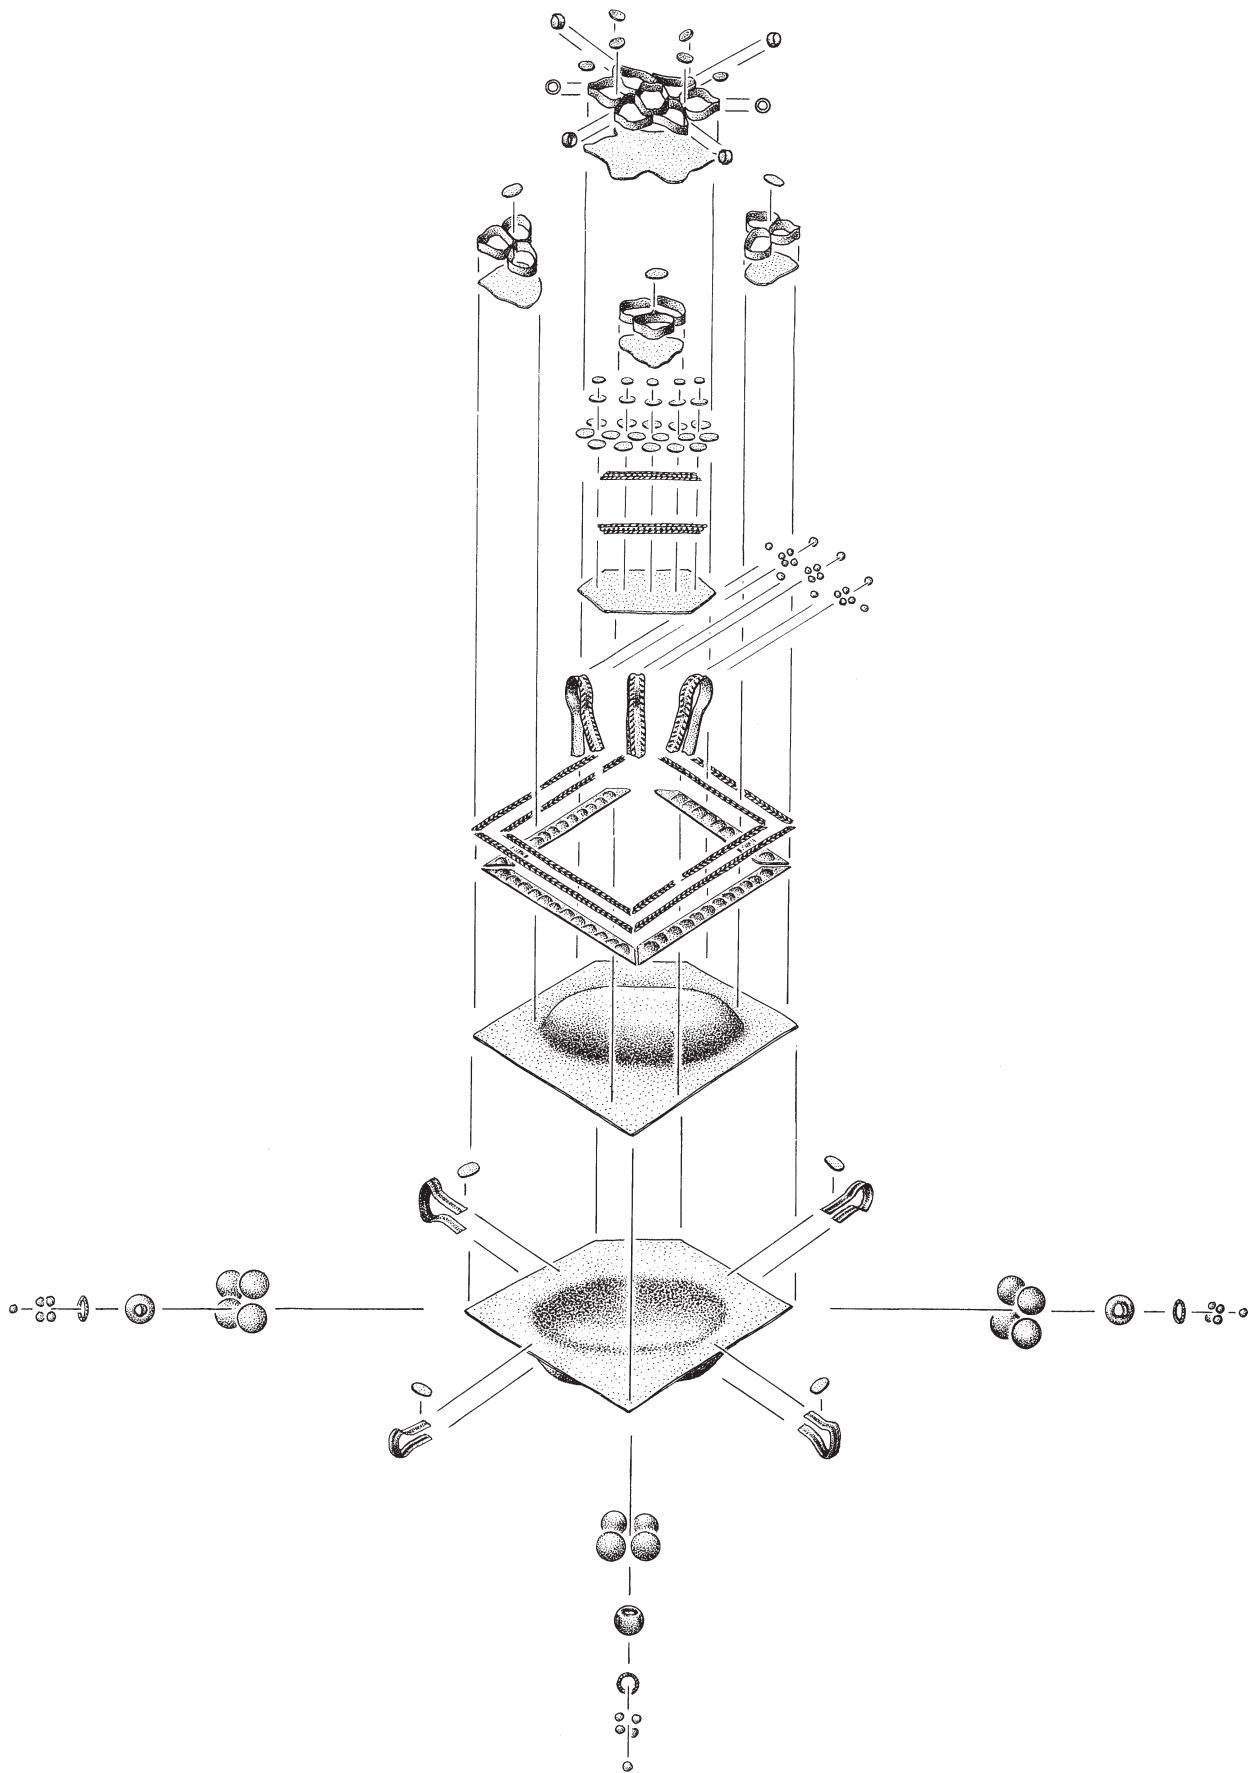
Kat. 23: Explosionszeichnung aller Einzelteile des rautenförmigen Goldanhängers, die in »Kompositstechnik« zusammen-
